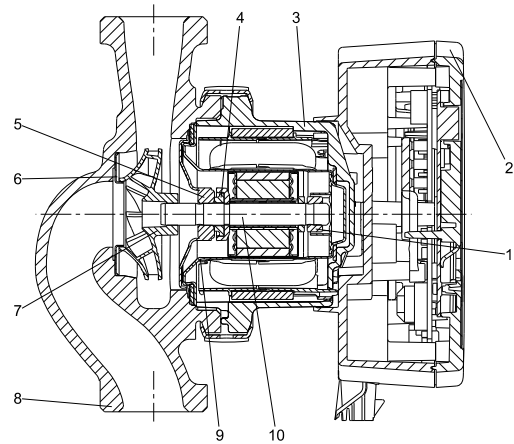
Модификация с резьбовыми соединениями и корпусом ротора из нержавеющей стали
